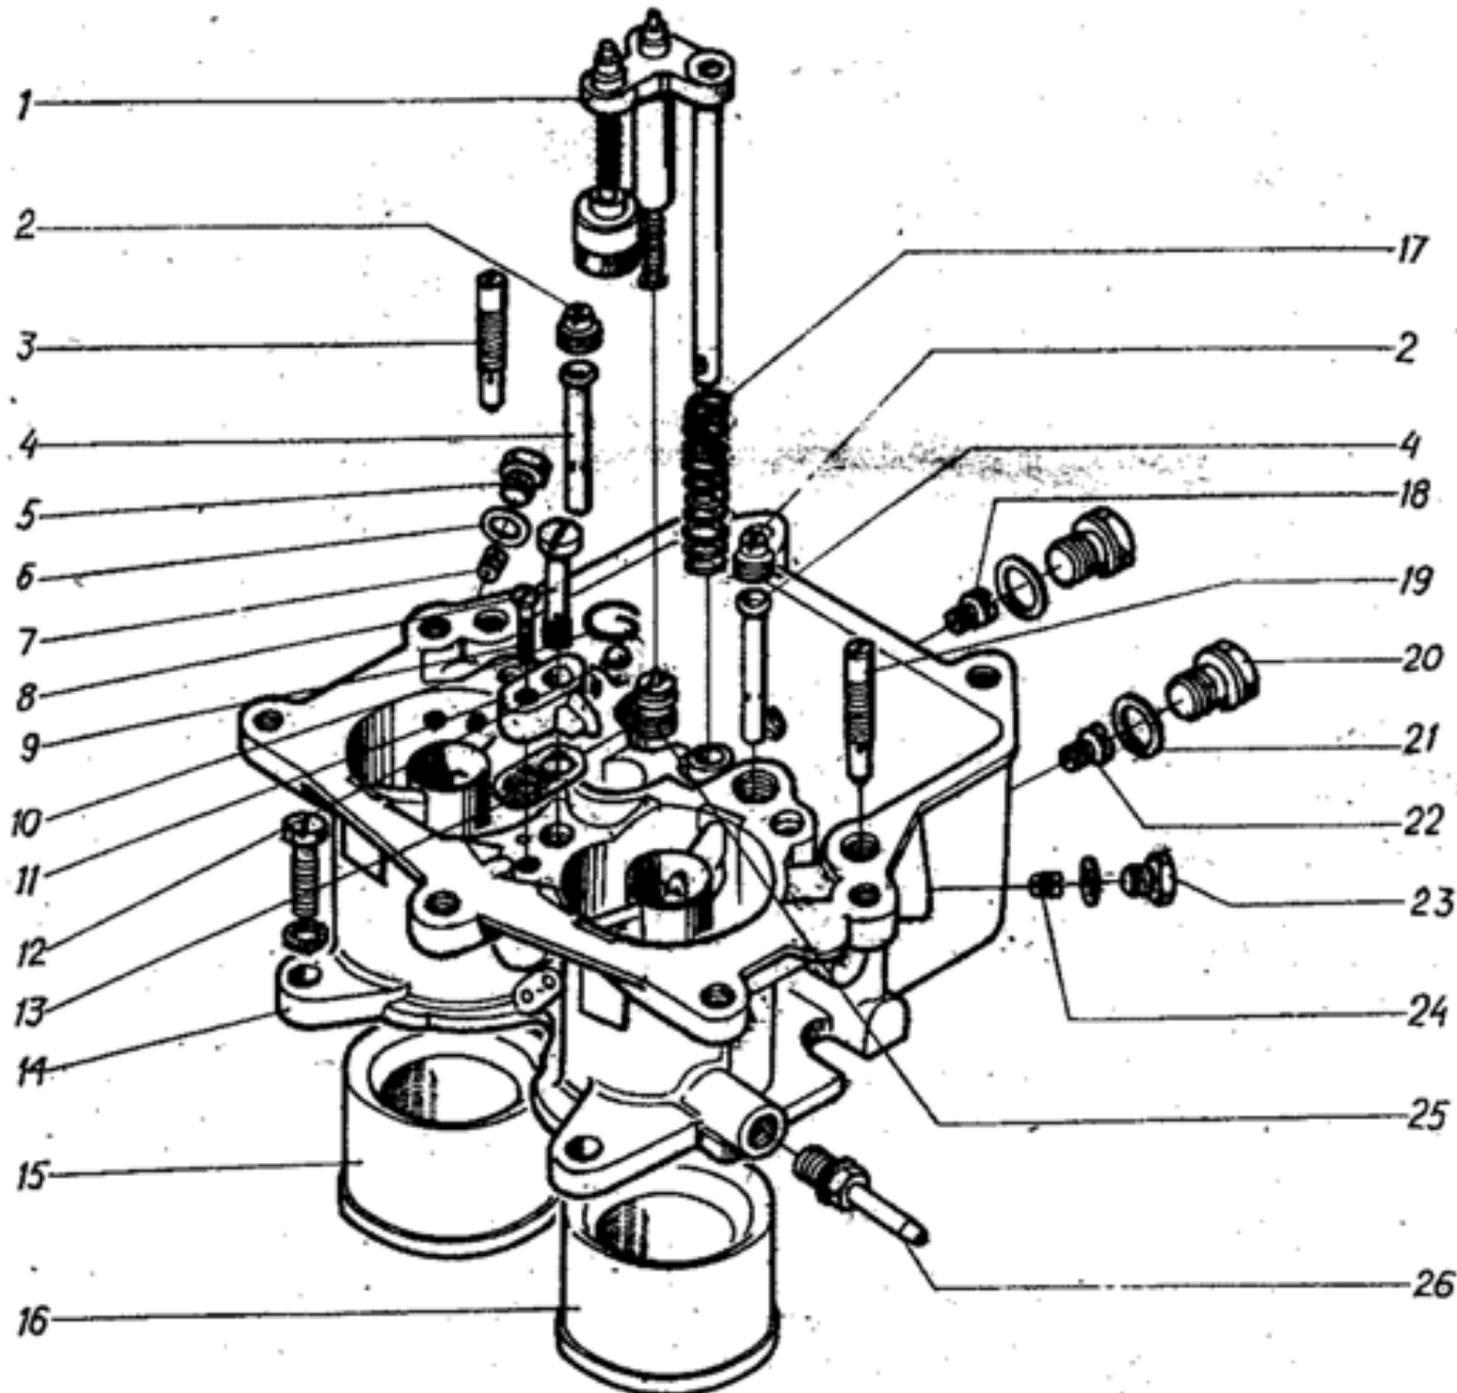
Детали корпуса поплавковой камеры: 1 - привод ускорительного насоса в сборе; 2 - воздушный жиклер главной дозирующей системы; 3 - топливный жиклер системы холостого хода левый; 4 - эмульсионная трубка; 5 - пробка резьбовая канала жиклера; 6 - прокладка; 7 - главный топливный жиклер левый; 8 - винт топливопроводящий; 9 - винт крепления распылителя; 10 - кольцо стопорное; 11 - распылитель; 12 - обратный клапан; 13 - прокладка распылителя; 14 - корпус поплавковой камеры; 15 - диффузор левый; 16 - диффузор правый; 17 - пружина привода ускорительного насоса отжимная; 18 - главный топливный жиклер левый; 19 - топливный жиклер системы холостого хода правый; 20 - пробка резьбовая канала жиклера; 21 - прокладка; 22 - главный топливный жиклер правый; 23 - пробка воздушного жиклера; 24 - воздушный жиклер системы холостого хода; 25 - клапаны экономайзера; 26 - патрубок привода вакуум-корректора
